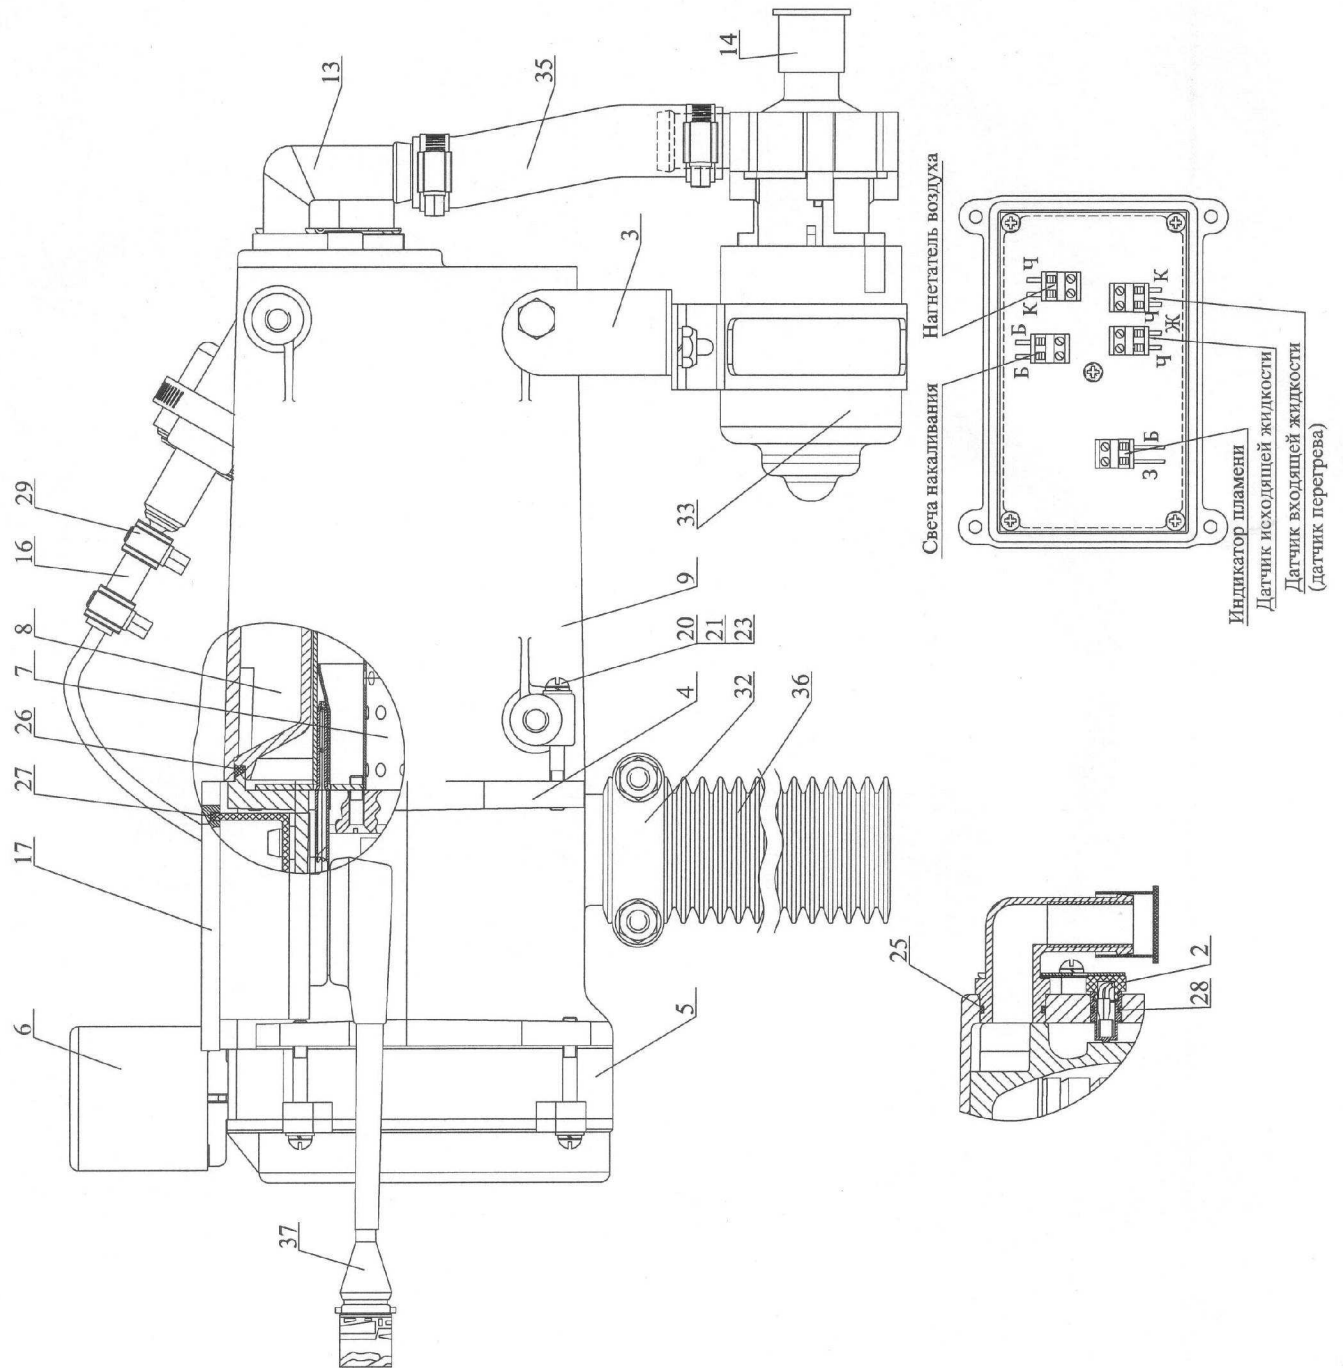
Подогреватель для автомобиля МАЗ - 12ЖД24.8106
